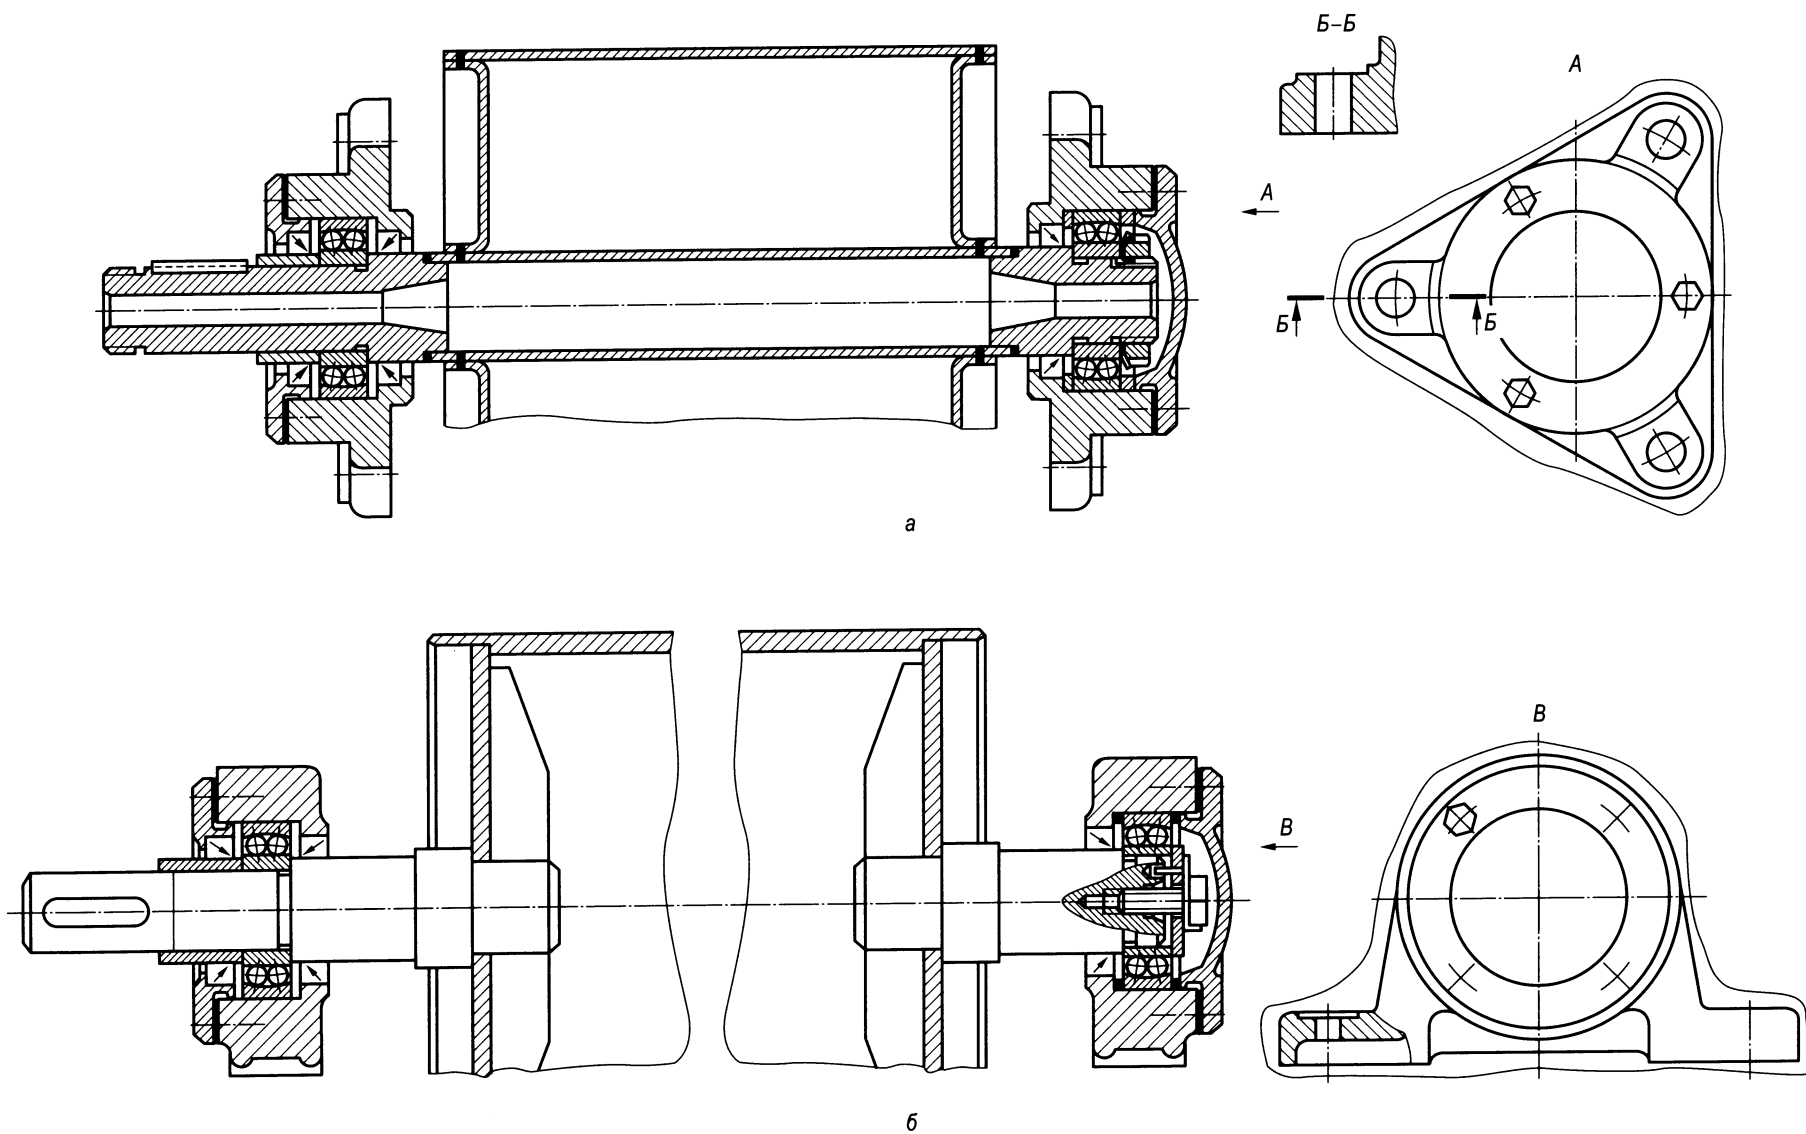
Сварной приводной вал-барабан из труб и штампованных деталей (а) и с цапфами (б)
